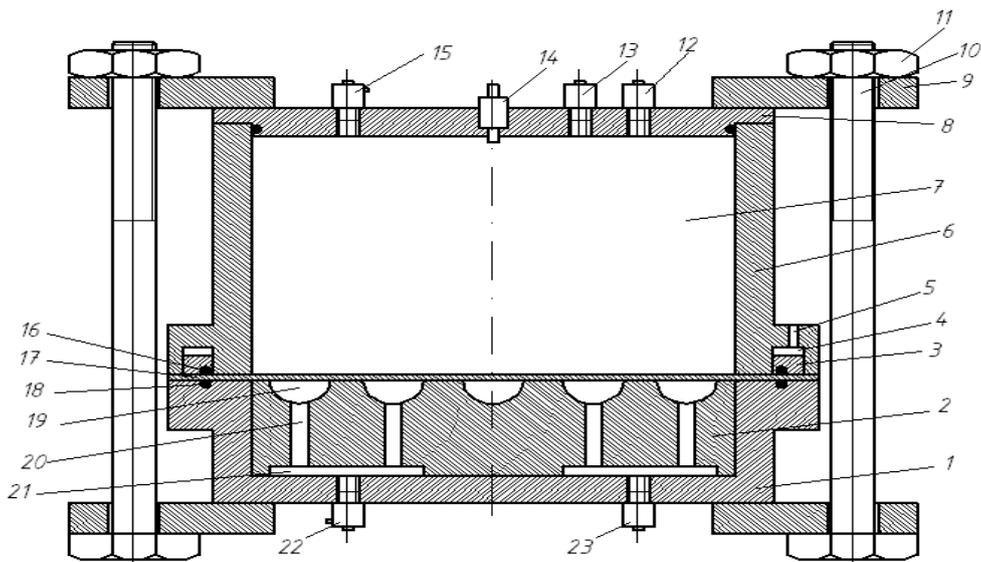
Схема устройства для газовой штамповки панели теплообменника: 1- матрицедержатель; 2- матрица; 3- кольцевой поршень; 4- кольцевая полость; 5- канал; 6- корпус; 7- камера сгорания; 8- крышка; 9 - плиты; 10- болт; 11- гайка 12, 23 - впускные клапаны; 13- предохранительный клапан; 14- свеча зажигания; 15, 22- выпускные клапаны; 16,18 - уплотнительные кольца 17- штампуемая заготовка; 19- спиральный канал; 21-кольцевая полость.
